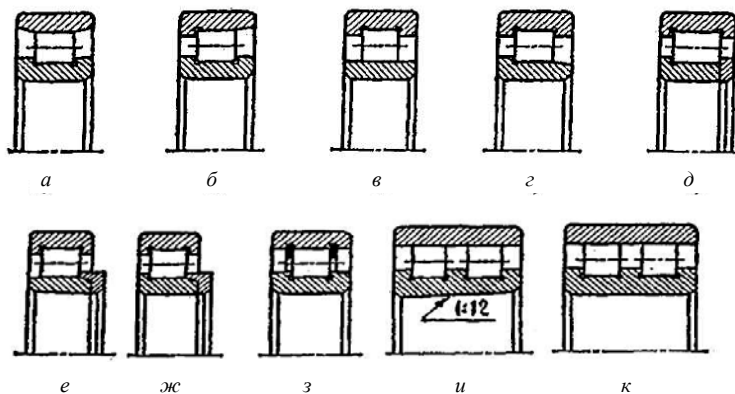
Роликоподшипники с короткими цилиндрическими роликами типов:
